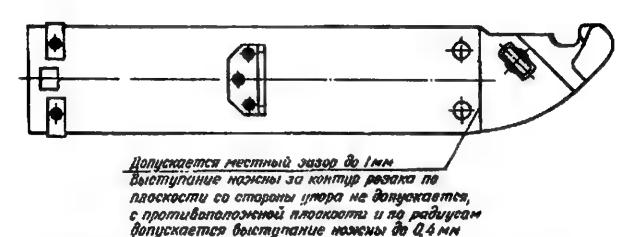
Устранение качки резака и соединении с корпусом ножных 49 · корпус пожны; 59 — резак; 59 — заклепка
